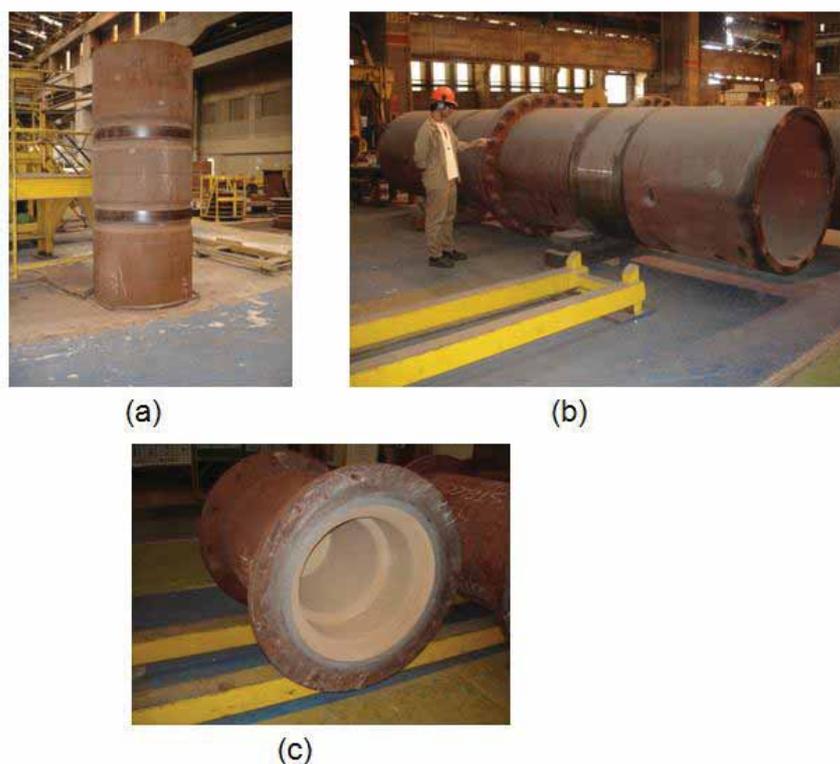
Molde para vazamento do cilindro: (a) coquilha; (b) *sleeve*; (c) caixa. (Fonte: Autor).
